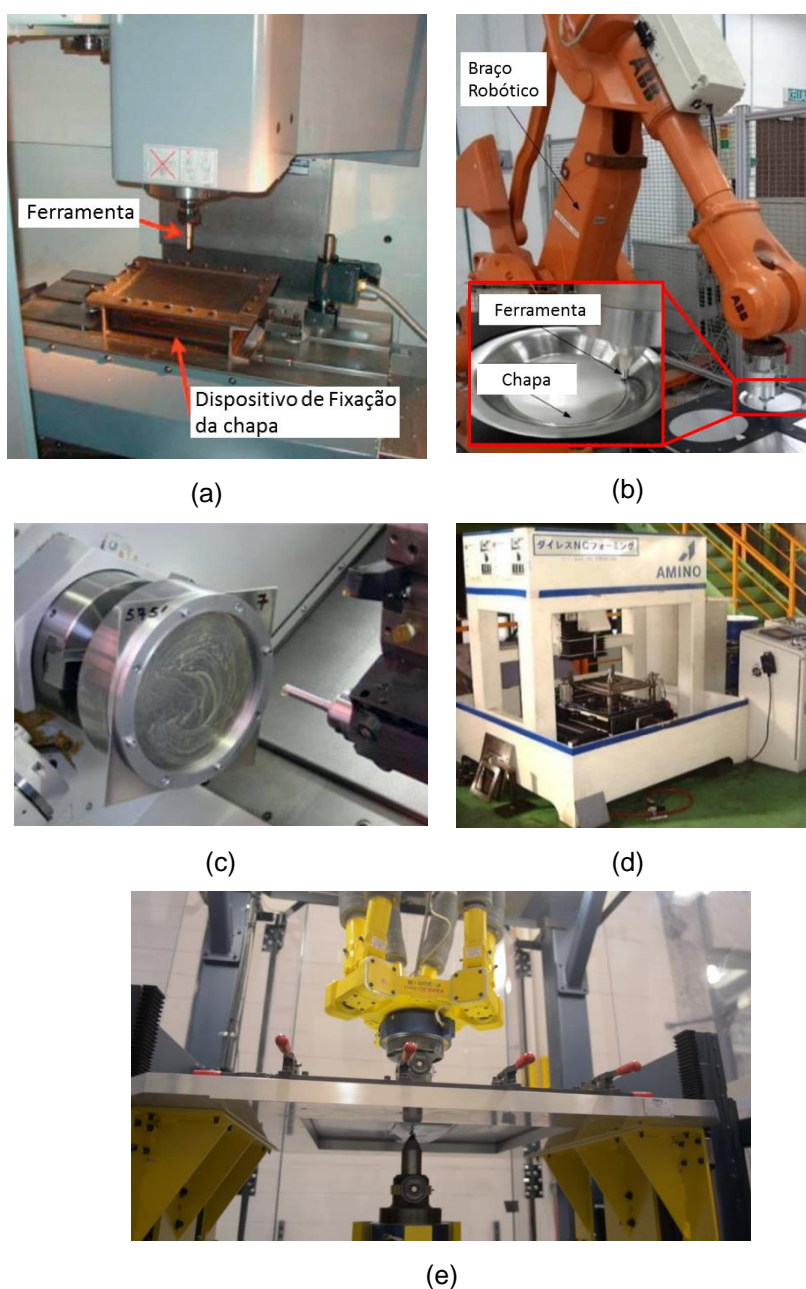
Máquinas de Estampagem Incremental: (a) Fresadora CNC [4], (b) Braço Robótico [35], (c) Torno CNC [4], (d) Máquina Amino Dedicada à Estampagem Incremental [1], (e) F3T Dedicada à Estampagem Incremental [36].
